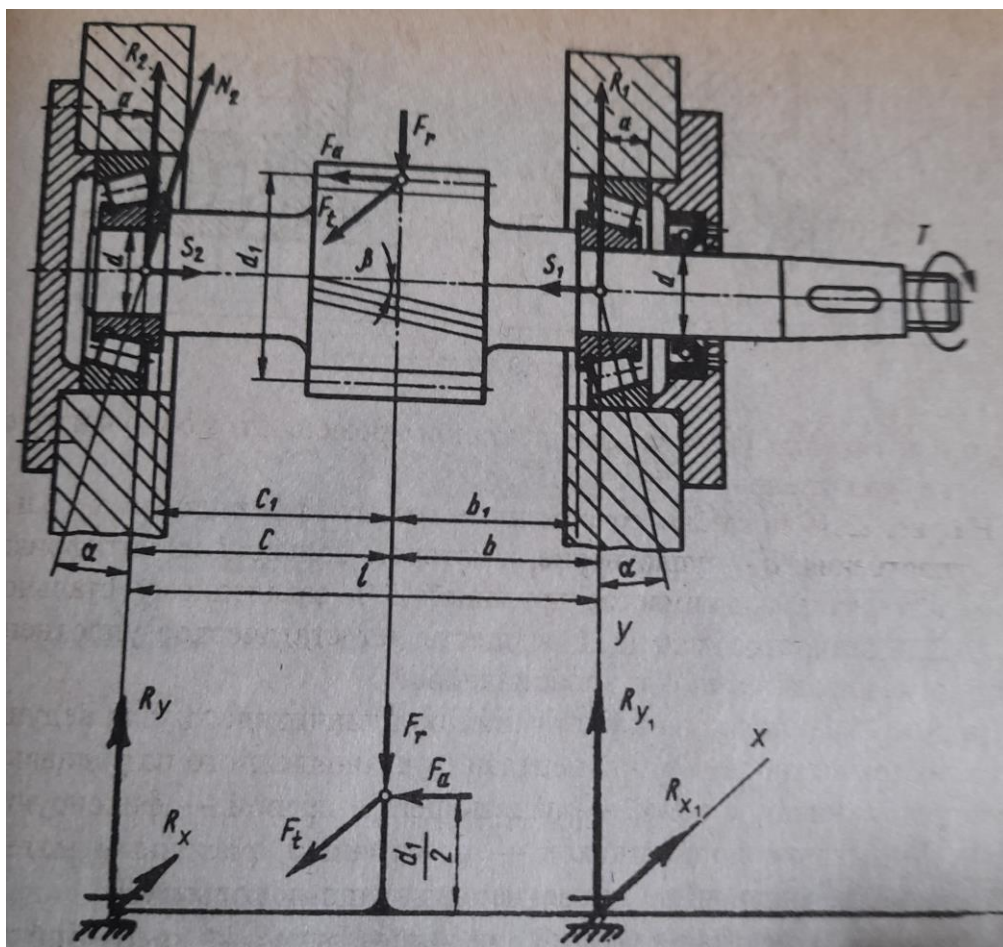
Расчетная схема вала цилиндрического редуктора
